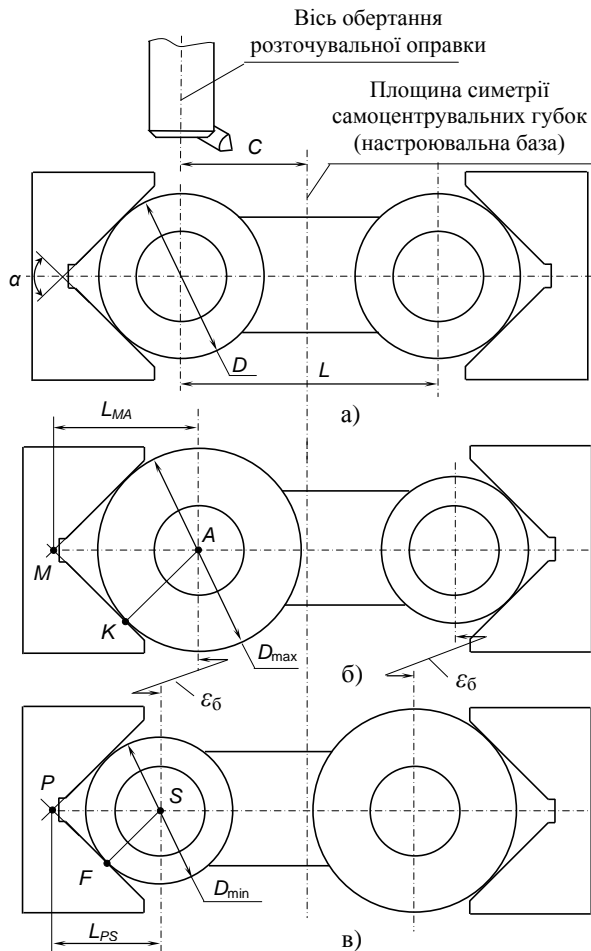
Розрахункова схема для визначення похибки базування як складової мінімального припуску для розточування отворів
